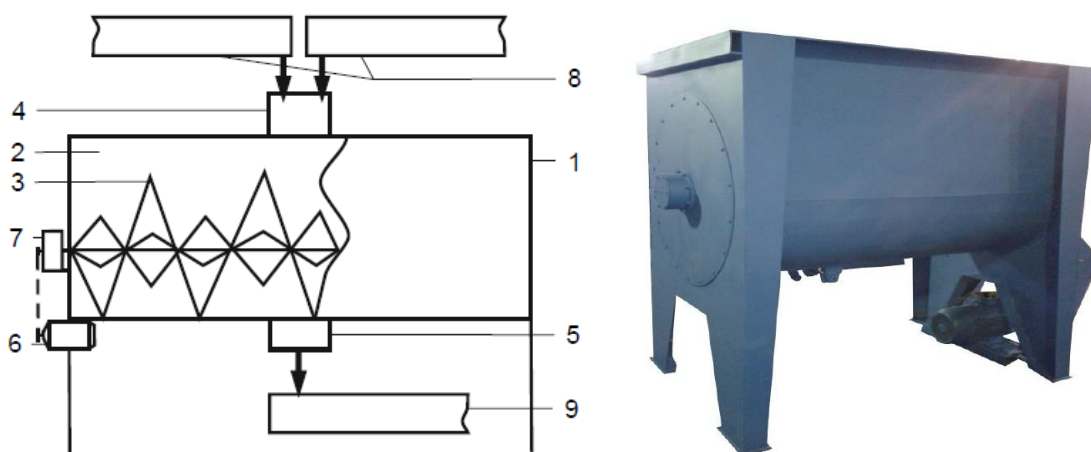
Конструктивная схема и общий вид смесителя
